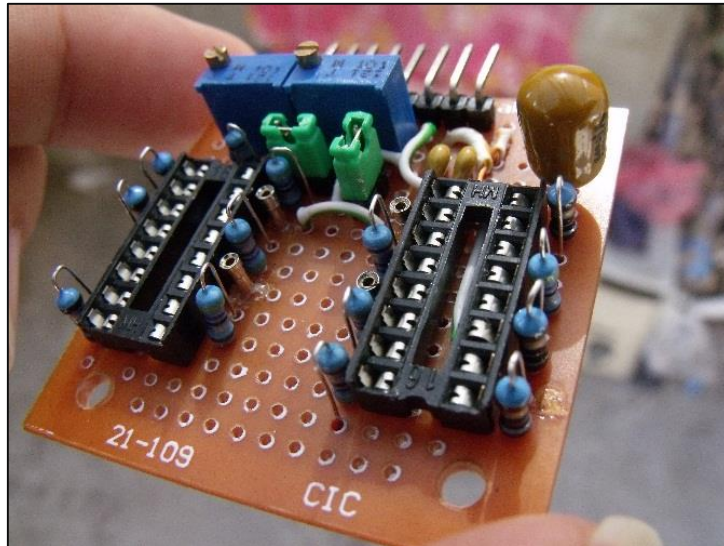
Proceso de soldado de la parte de auto calibración.
